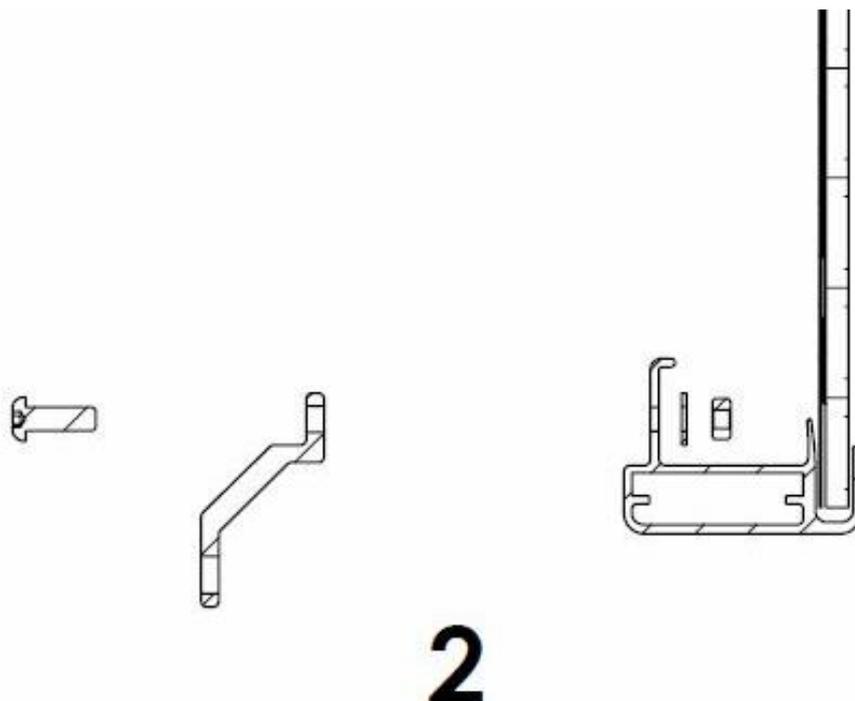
Detailansicht (Schnitt) zur Montage von zwei Wandhalterung Laschen
